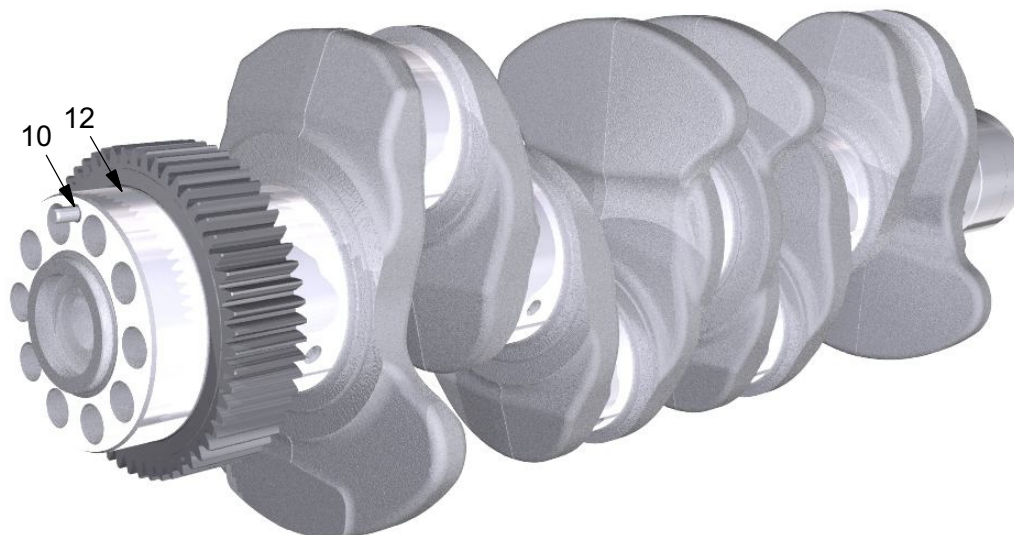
Вал коленчатый (Лист 3 из 3)
